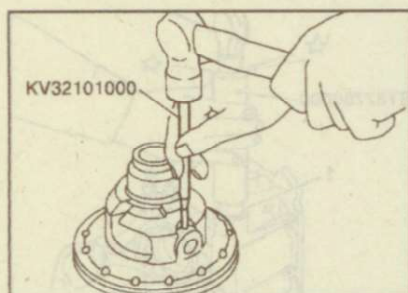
Установка цилиндрического штифта крепления оси сателлитов
